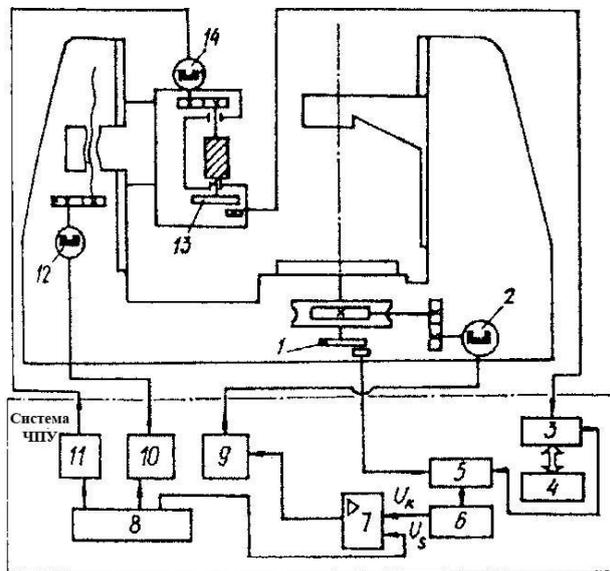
Структурная схема зубофрезерного станка с ЧПУ и разомкнутой кинематикой
